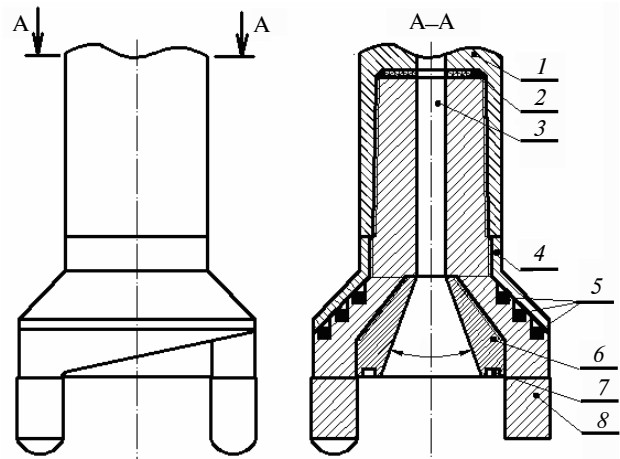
Різець кавітаційний із фрагментом бурової штанги: 1 – фрагмент бурової штанги; 2 – прокладка гумова; 3 – канал підвідний; 4 – кожух; 5 – магніт; 6 – насадка дифузорна; 7 – паз монтажний; 8 – вставка твердосплавна
